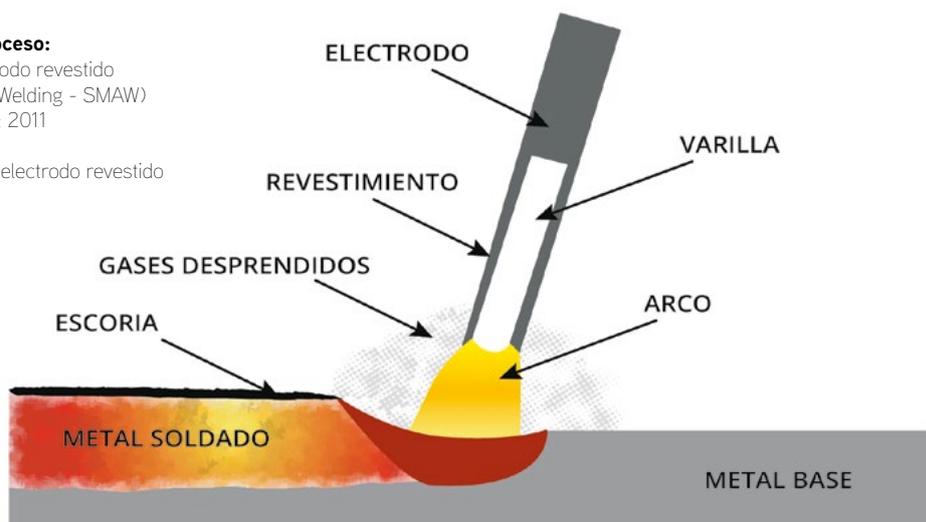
Procedimiento de soldadura con electrodo revestido
